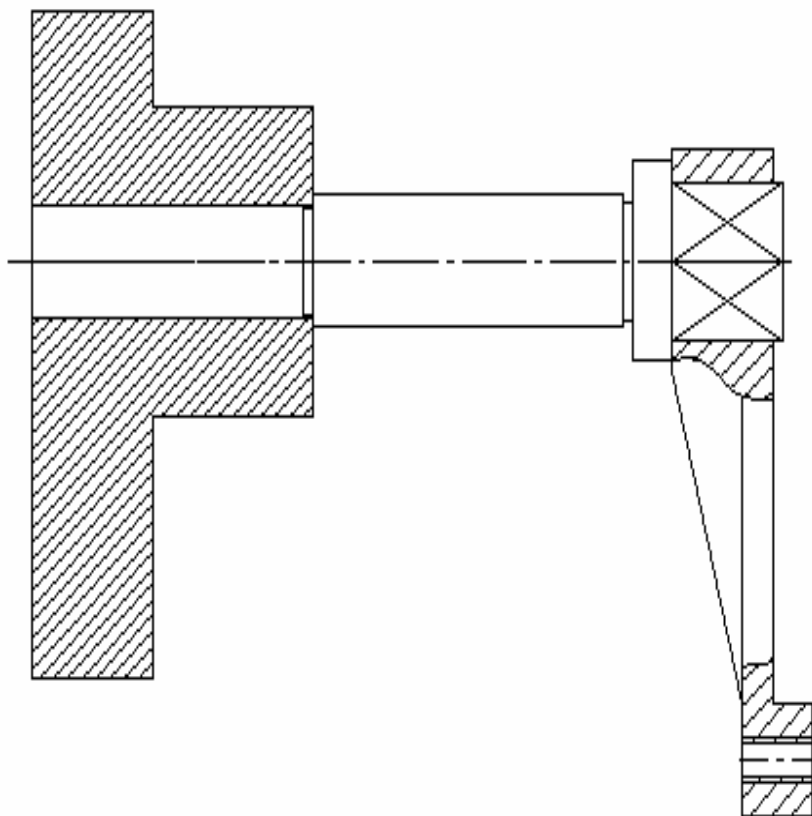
Часть сборочного чертежа кулачкового механизма.
